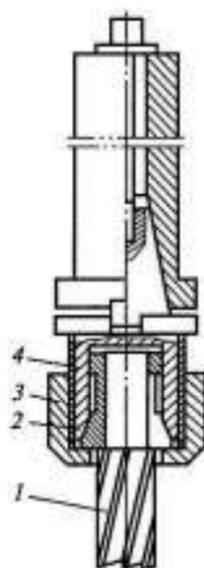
Установка концевых фрез с цилиндрическим хвостовиком в патроне:
